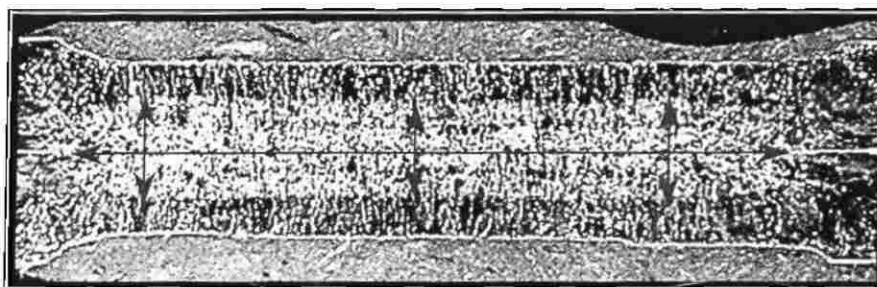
Medición de a) Penetración de la soldadura. b) Diámetro del botón.
